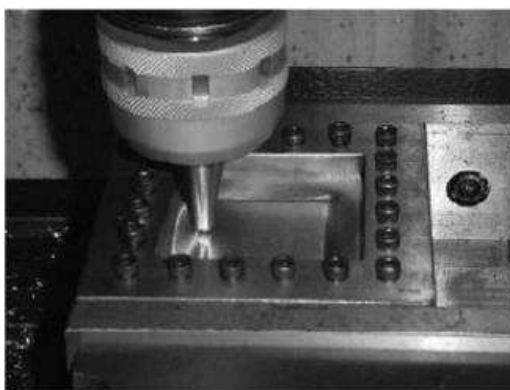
Exemplo de Estampagem Incremental por CNC (KIM et al, 2002)
